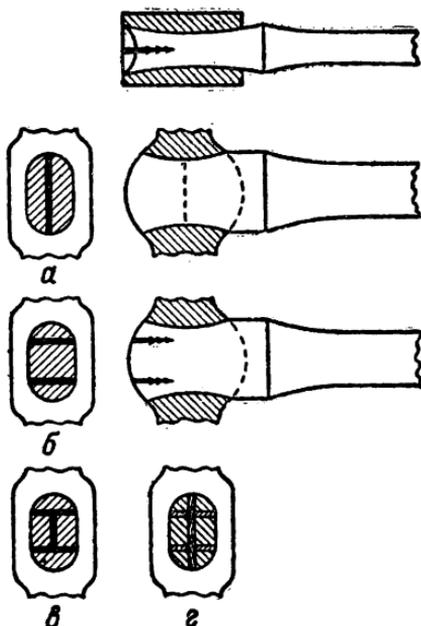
Расклинивание конца ручки молотка и кувалды деревянными или стальными клиньями.
